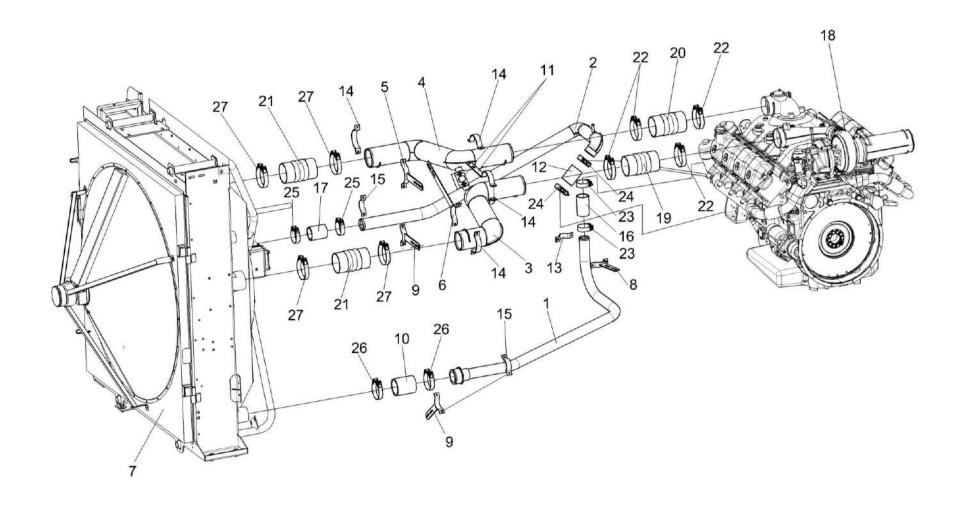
Установка двигателя ОМ 502LA КВК 0150000 (установка блока радиаторов)
